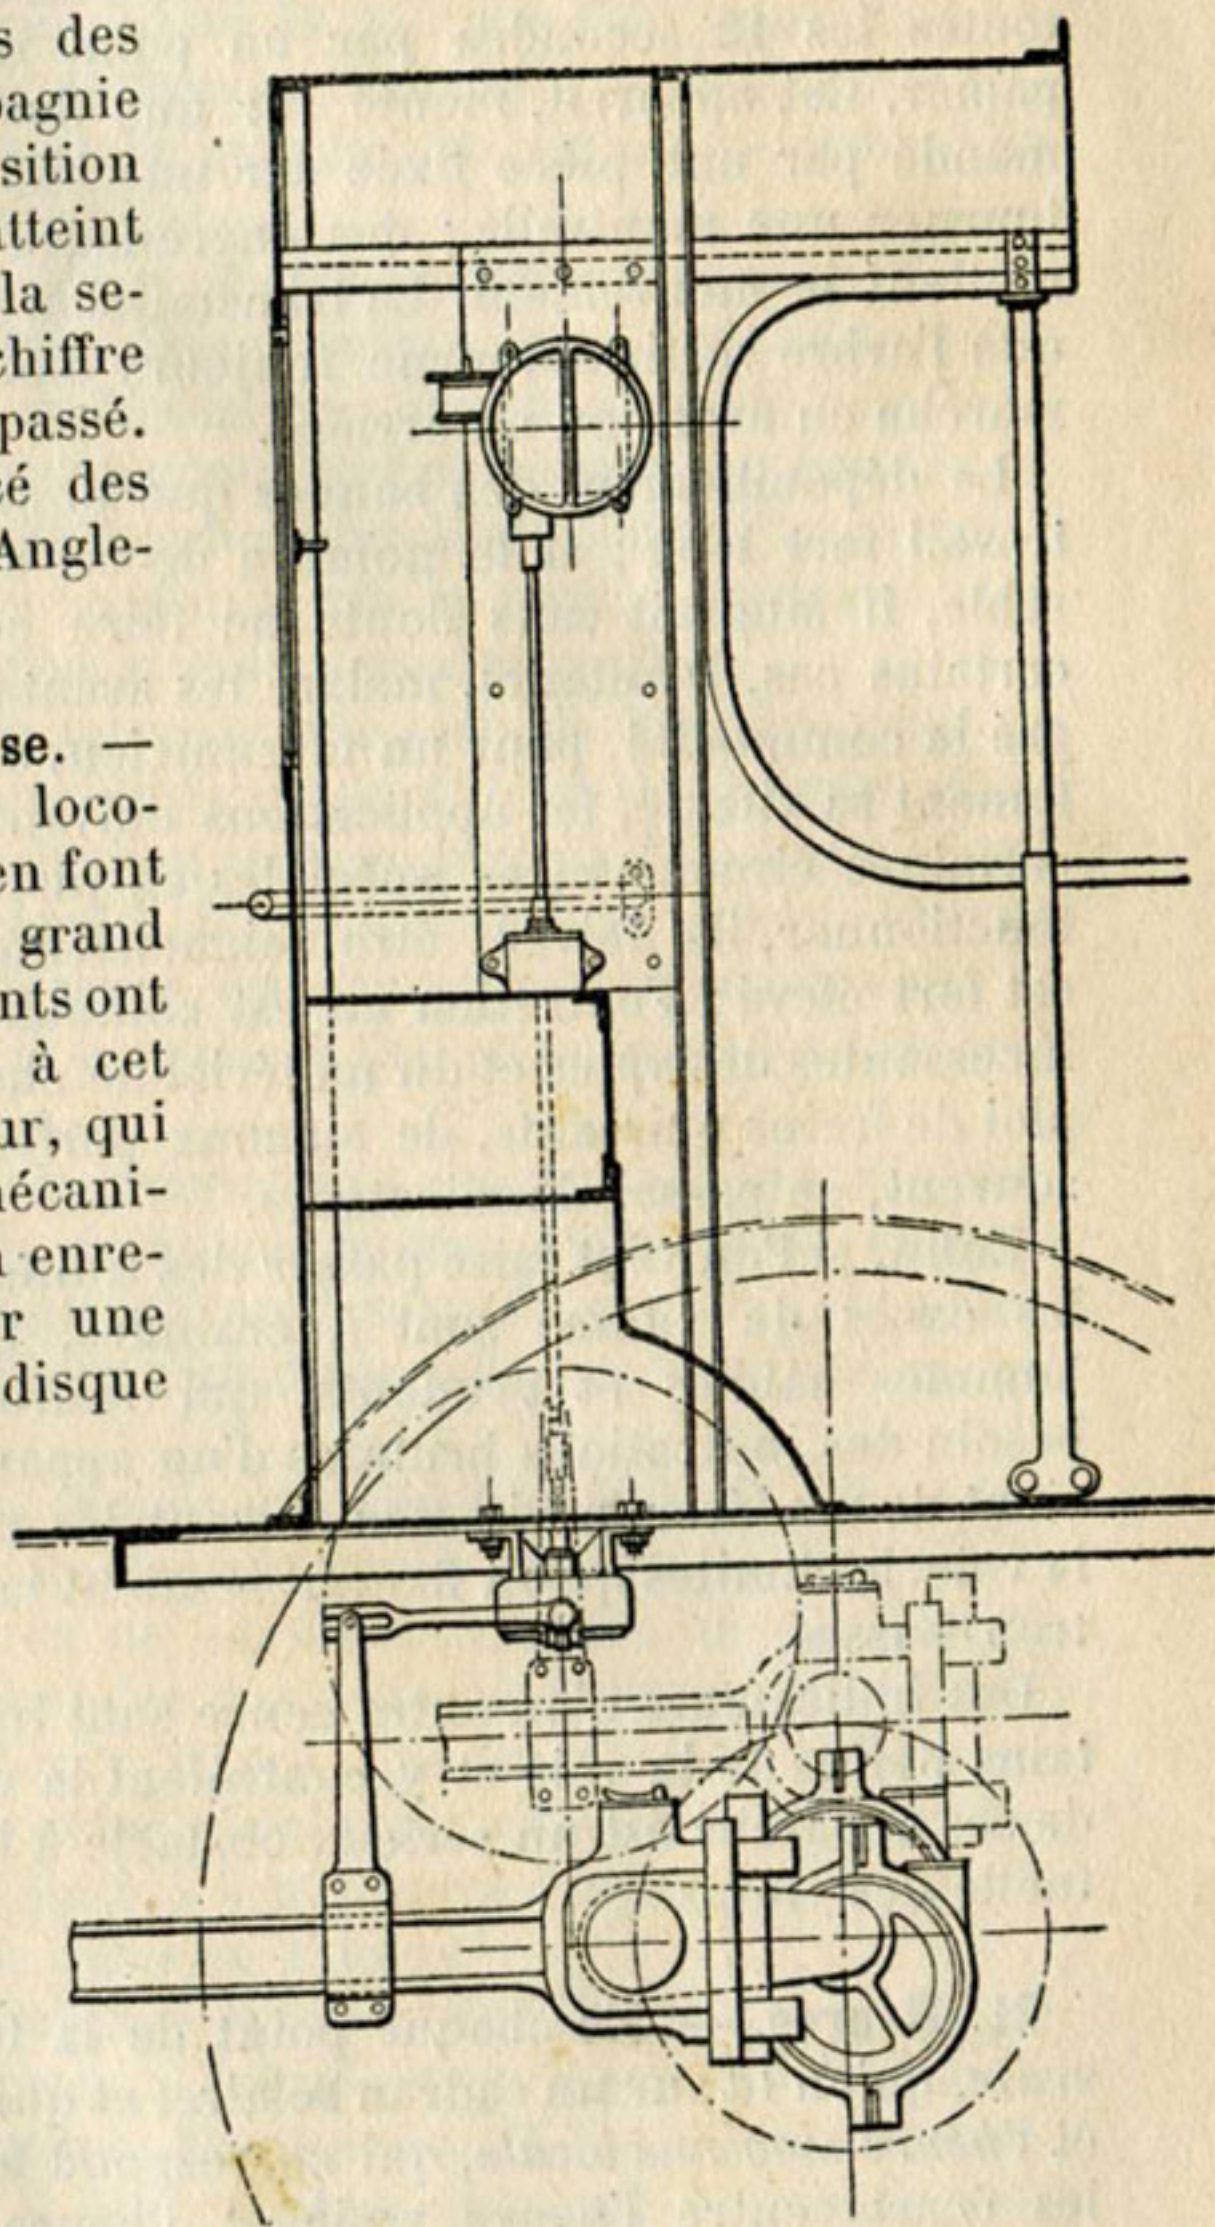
Montage de l'indicateur de vitesse Hausshaelter sur une locomotive des chemins de fer de l'Est (série 813 à 840).
